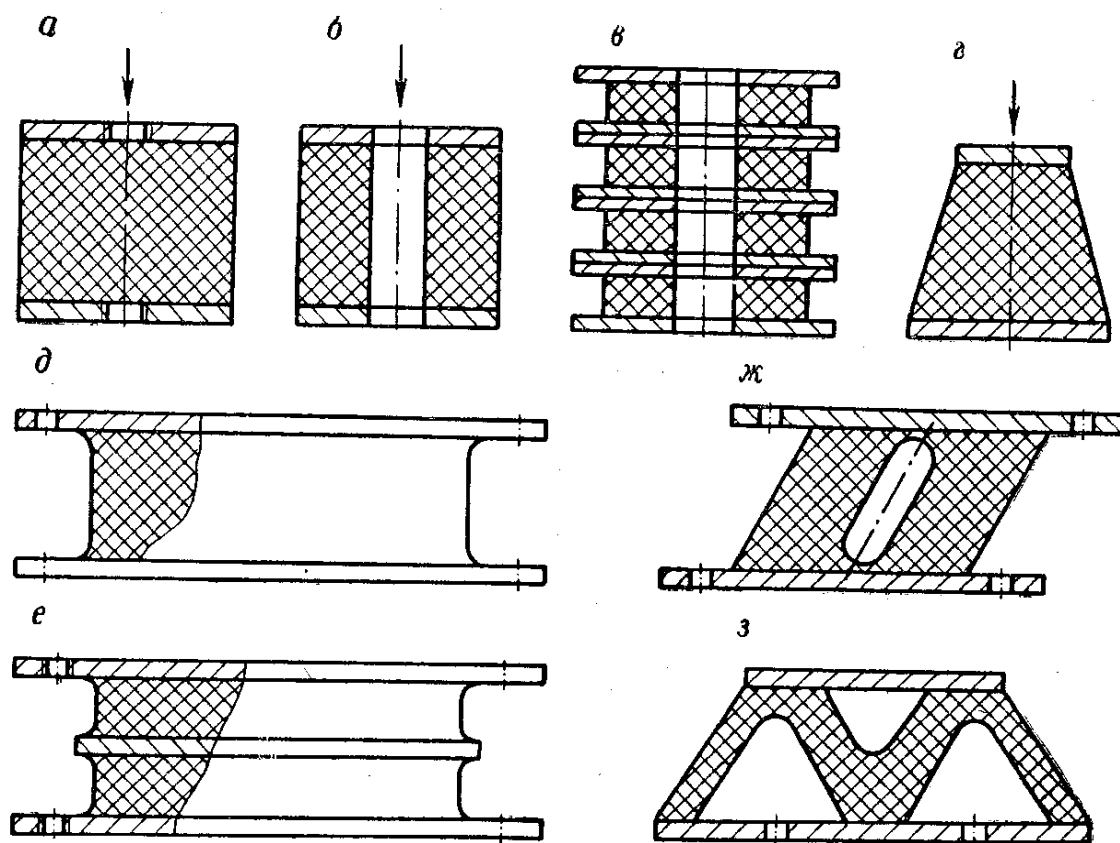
Гумометалеві деталі простої форми : а, б, в - циліндричної форми; г - конічної форми; д, е - квадратної або прямокутної форми; ж, з - з порожнинами.
